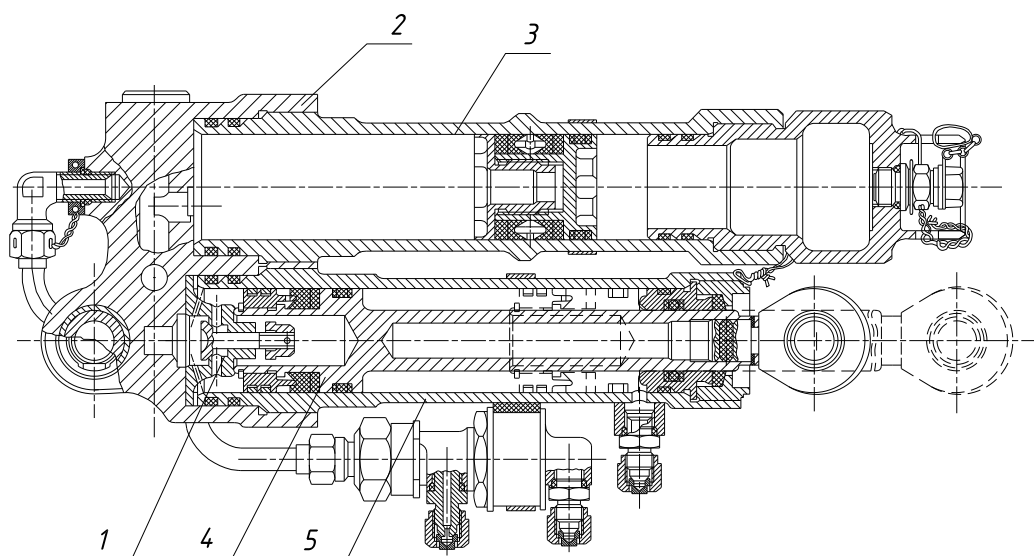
Пневмогидравлическая однопоршневая однокамерная рессора:
